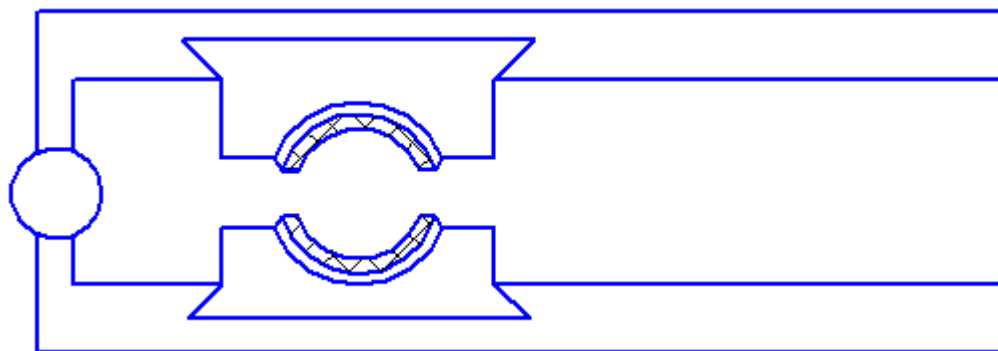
Эскиз клещей для прижима металлической оболочки к шейкам коленчатого вала
